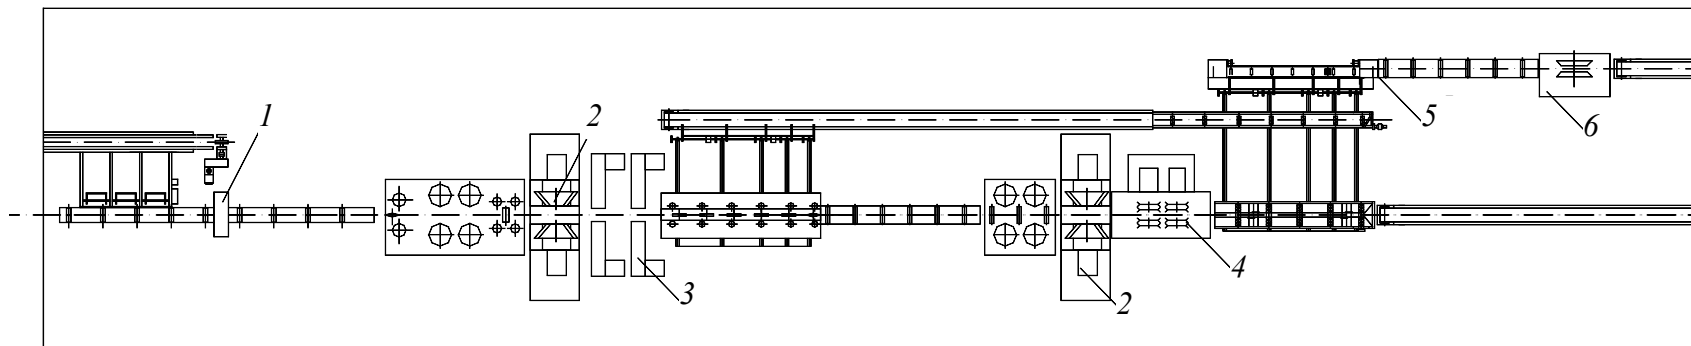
Схема расположения оборудования в цехе на базе ленточнопильных и круглопильных станков с фрезерными модулями:
